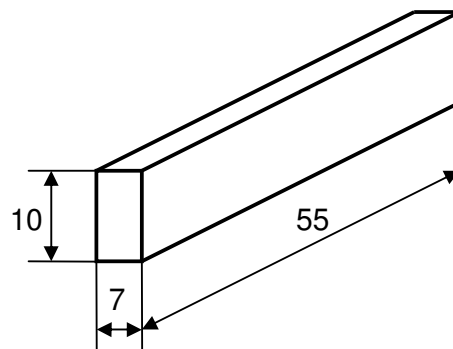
Dimensões do corpo de prova para o ensaio de impacto.
